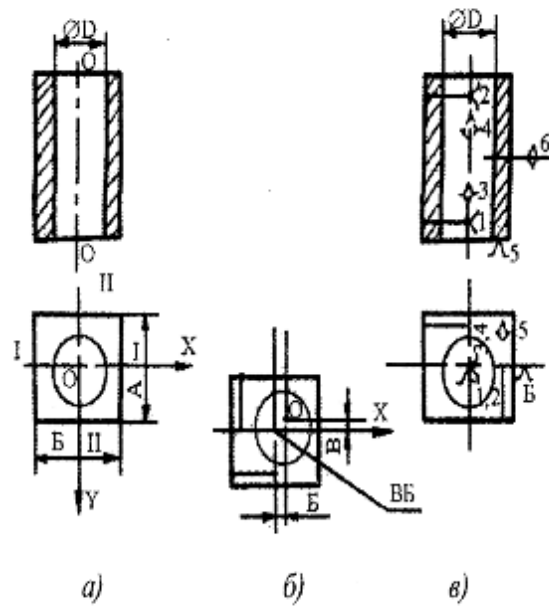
До розробки теоретичної схеми базування з використанням умовних баз
